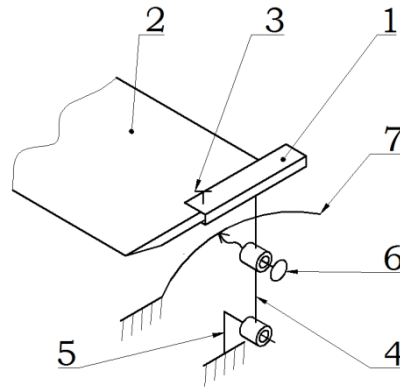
Кінематична схема пристрою для регулювання установки леза ножа
